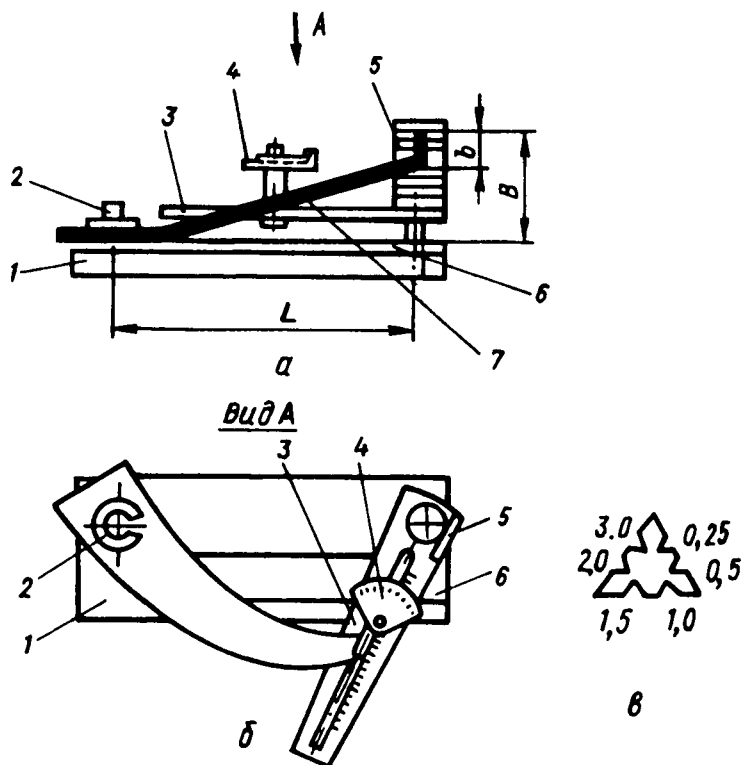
Устройство УПК для контроля параметров короснимателя:
